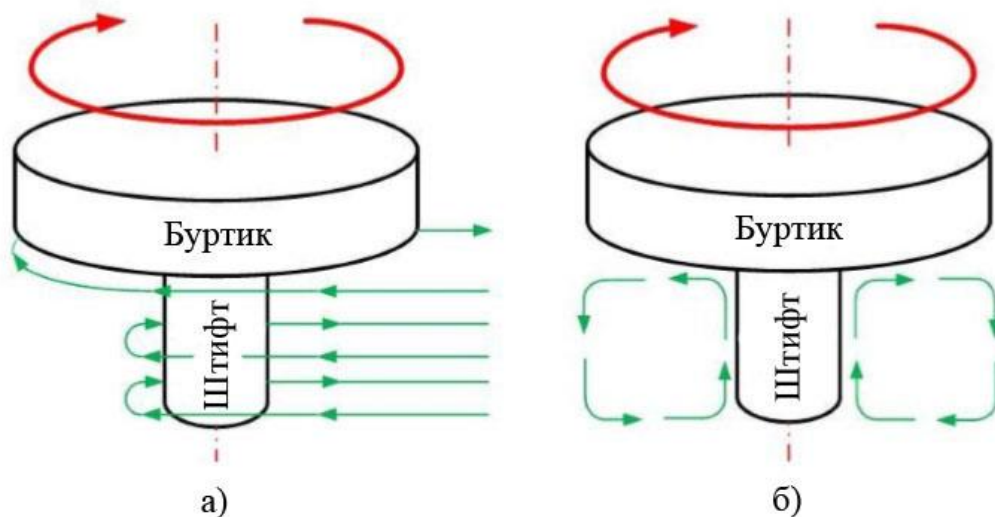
Направление потока металла во время сварки, а) горизонтальный поток металла; б) вертикальный поток металла
